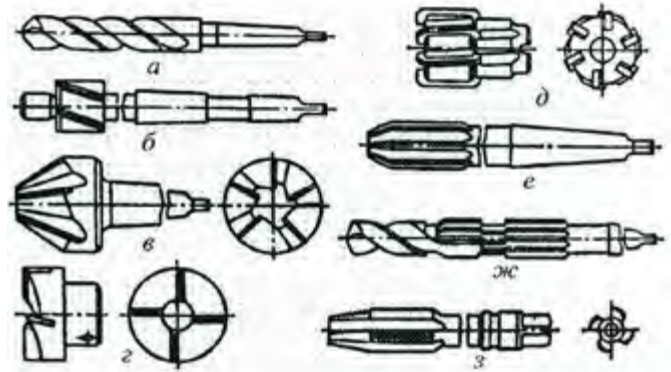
Інструменти для оброблення отворів на свердильних верстатах
